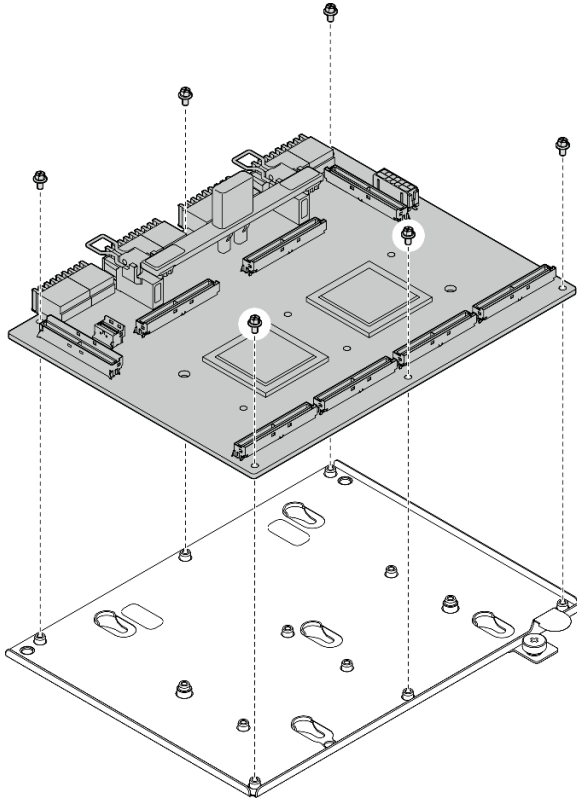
Desensamblaje de la Placa de conmutador PCIe de SXM5
